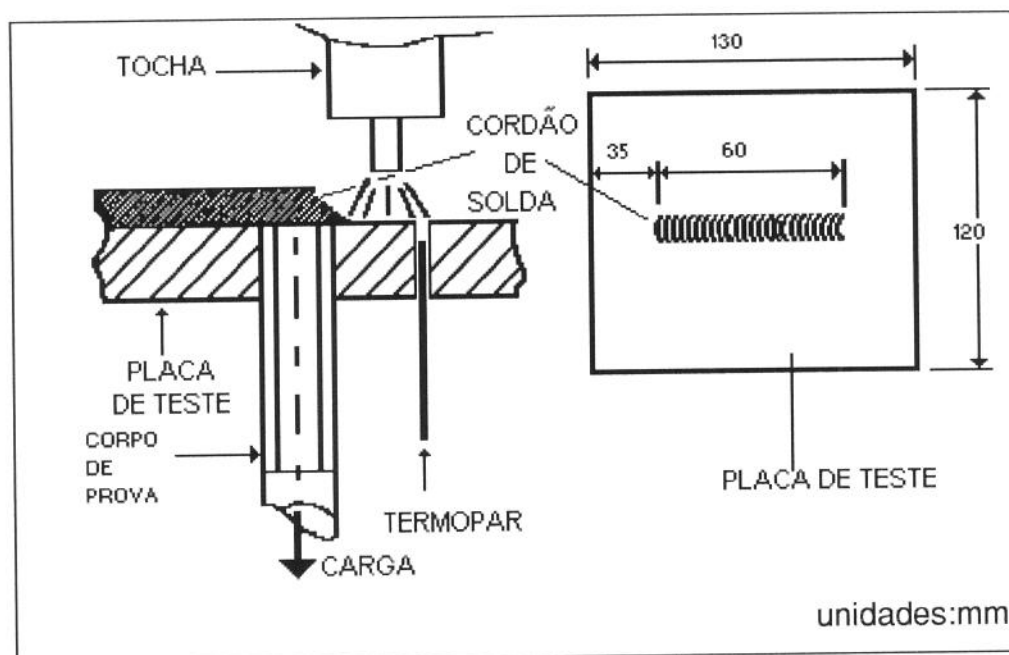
Esquema de fixação do corpo de prova à placa de teste e detalhamento das dimensões da placa e do cordão [13].
